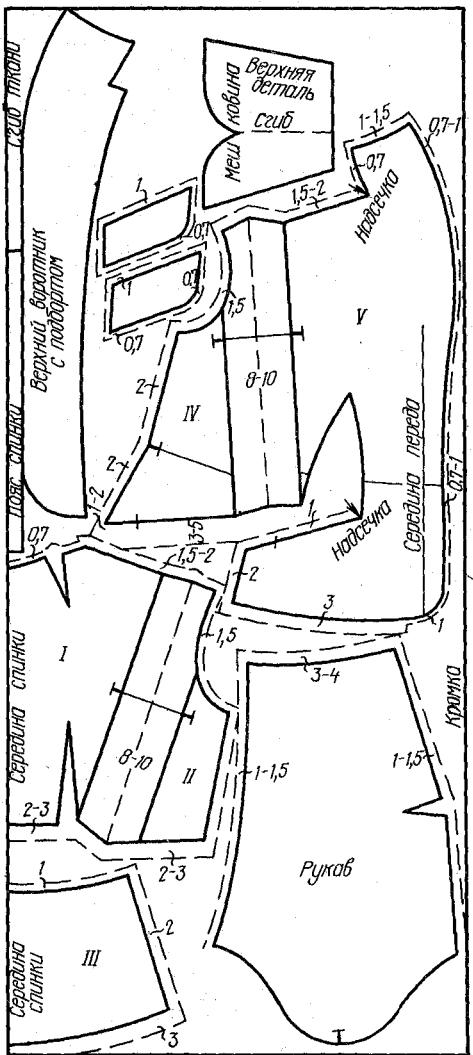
Раскладка выкроек на ткани и раскрой платья-костюма со складками от плеча
